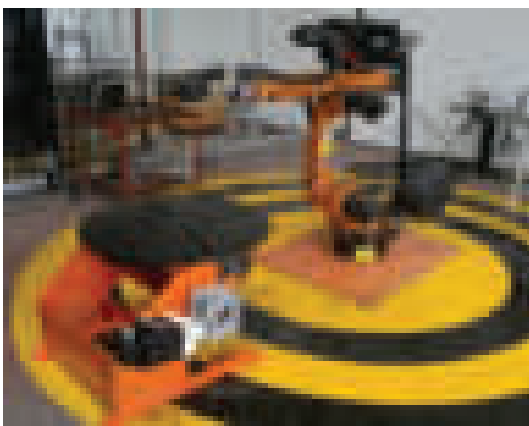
Mesa posicionadora de soldadura en dos ejes para el brazo robótico KUKA KR5ARC
